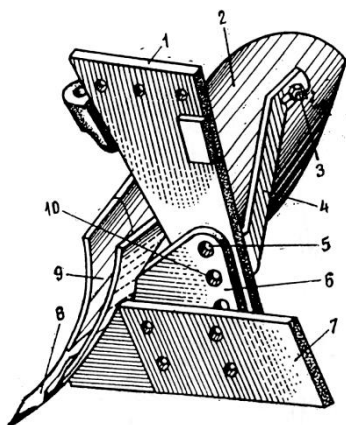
Культурный корпус: 1 – стойка; 2 – крыло отвала; 3,5,10 – болт с гайкой и шайбами; 4 распорка; 6 – башмак; 7 – полевая доска; 8 – лемех; 9 – грудь отвала
